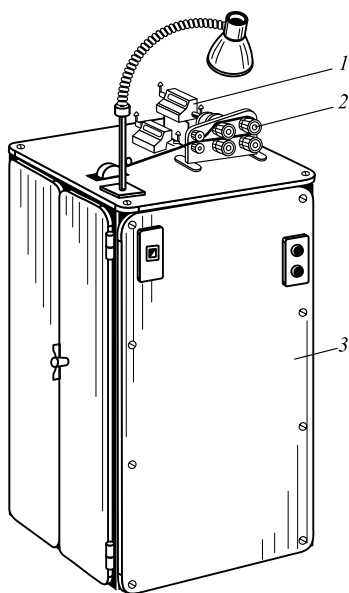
Механизм для резки и отсчета заготовок проводов:
